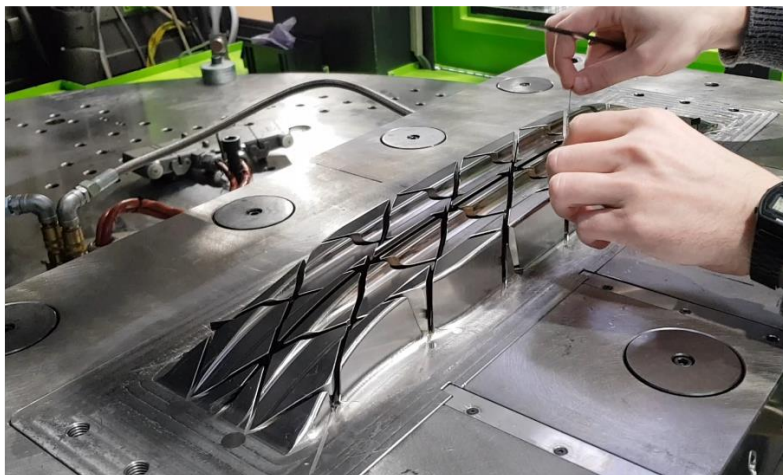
Manuelles Einbringen der Tapeeinleger in das Werkzeug
